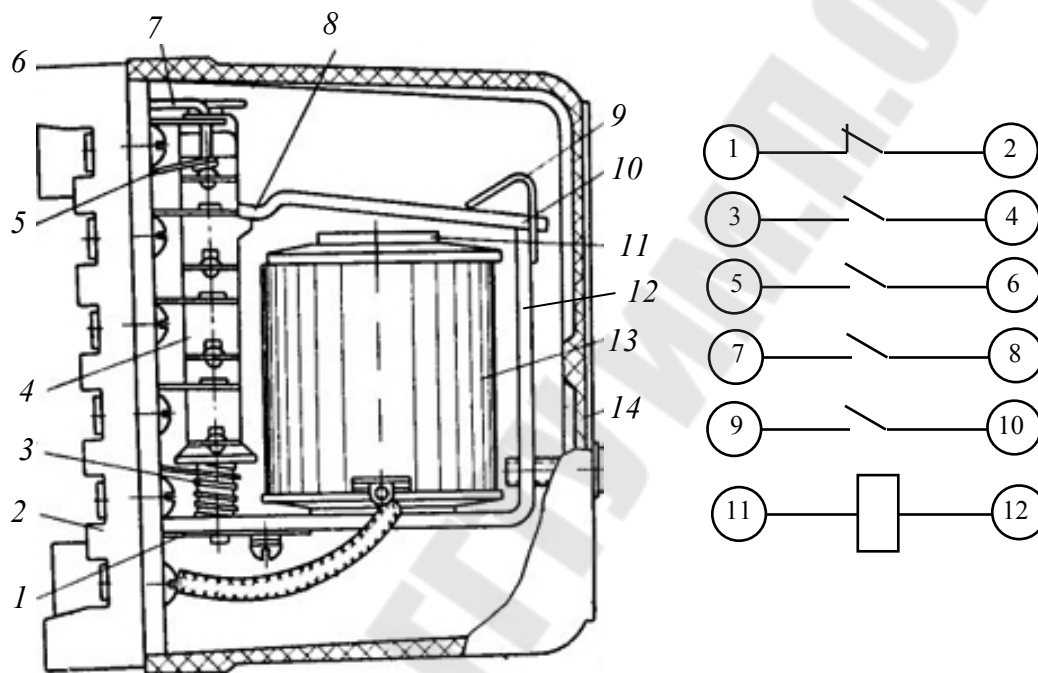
Общий вид и схема внутренних соединений промежуточного реле типа РП-23
